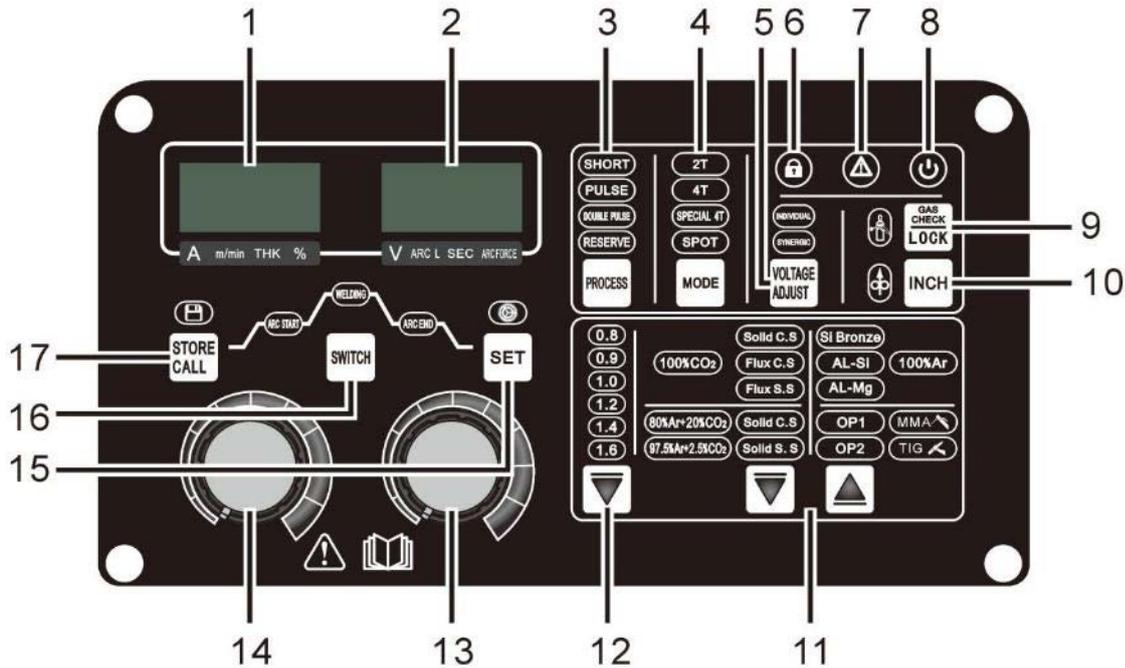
Panel de la fuente de soldadura por arco
